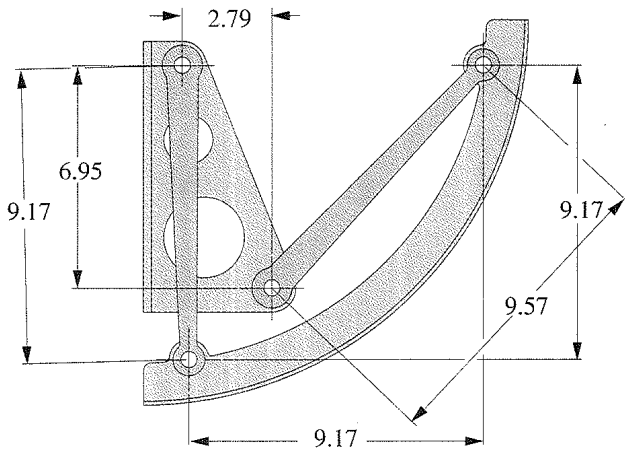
Problema 2-43 Mecanismo de arco de equipaje elevado de avión; dimensiones en pulgadas
